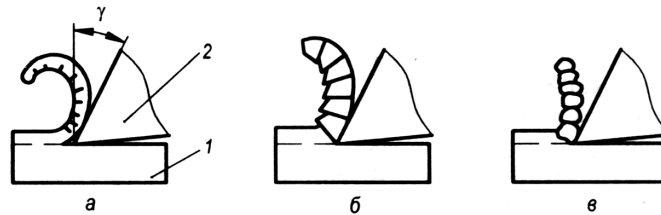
Вид стружки: стрічкоподібна (а); відколювана (б); надламана (в); 1 - заготовка; 2 - різець; γ - передній кут різця
